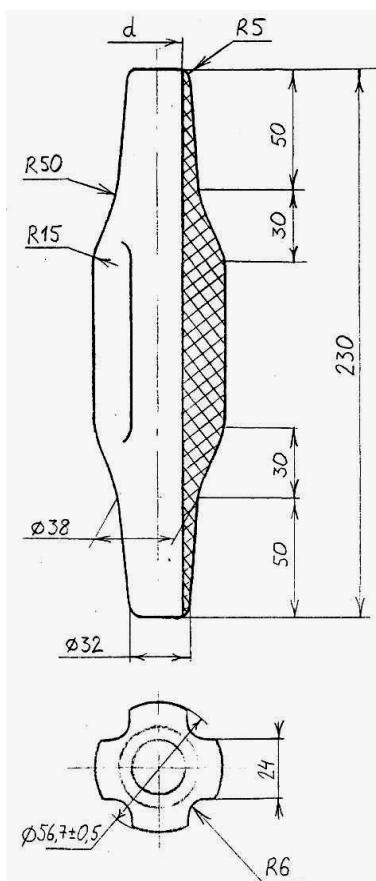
Конструкція скребка для надійного зчеплення з тілом штанги
